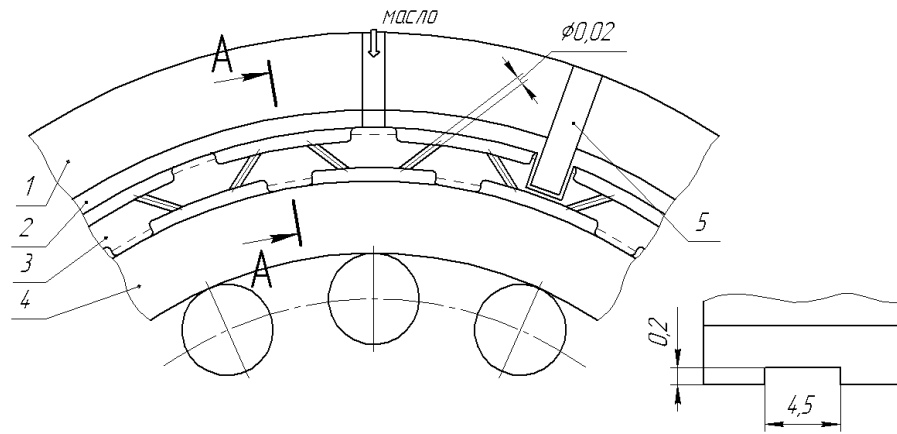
Дроссельный демпфер: 1 – корпус подшипника; 2 – втулка стальная; 3 – втулка Аллисона; 4 – наружное кольцо подшипника; 5 – штифт, фиксирующий вибратор от поворота
